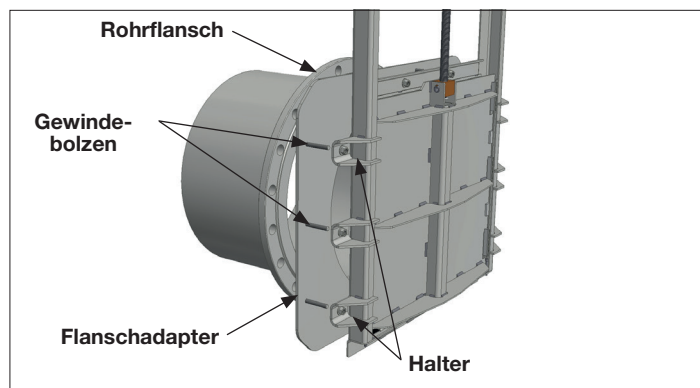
Montage des Spindelschiebers auf der Adapterplatte
